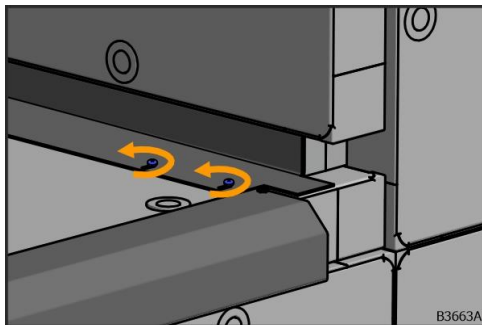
desserrage des vis de raccordement de la cornière d'étanchéité
